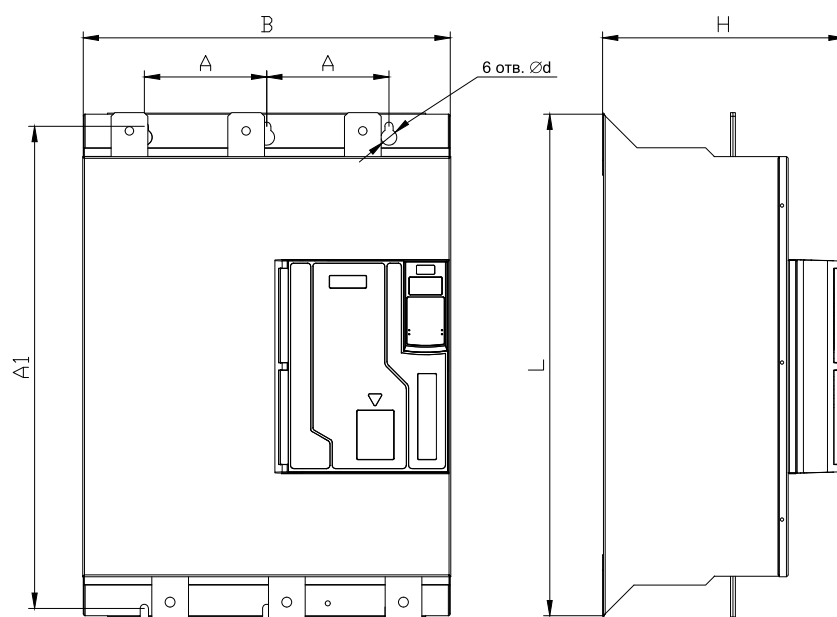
Габаритные и установочные размеры УПП, габарит 4
